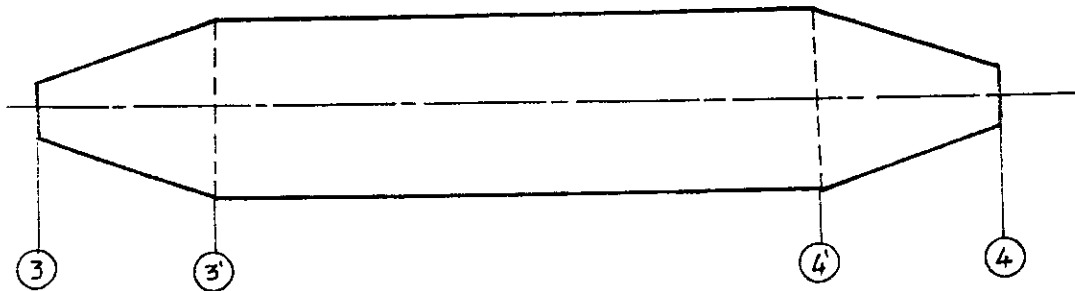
Dimensionnement de la chambre de combustion.
